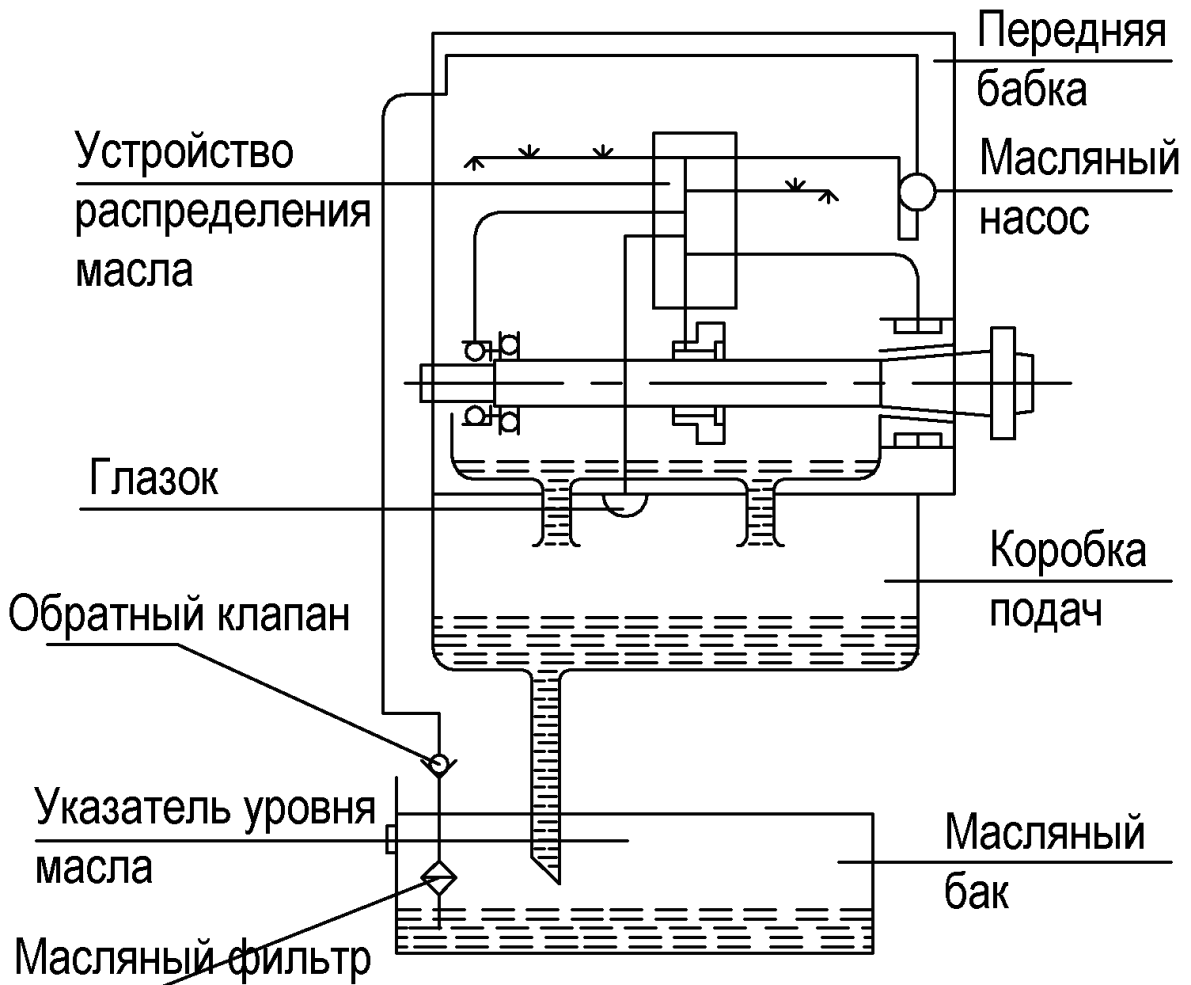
Схема смазки шпиндельной бабки станка и коробки подач
